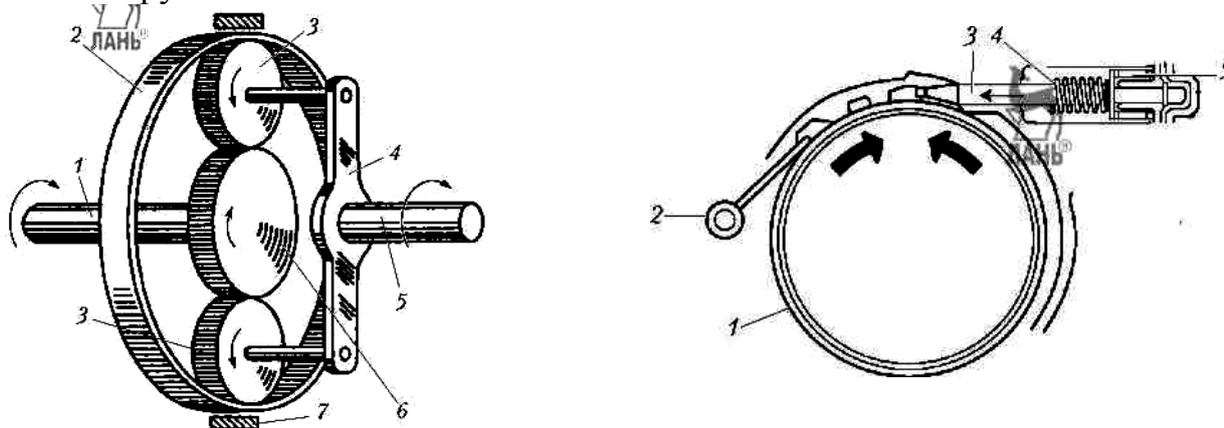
Планетарный механизм: Рис.3.4. Ленточный тормоз в сборе: 1 — ленточный тормоз; 2 — анкерная стяжка; 3 — шток поршня. 4 — пружина; 5 — поршень.
